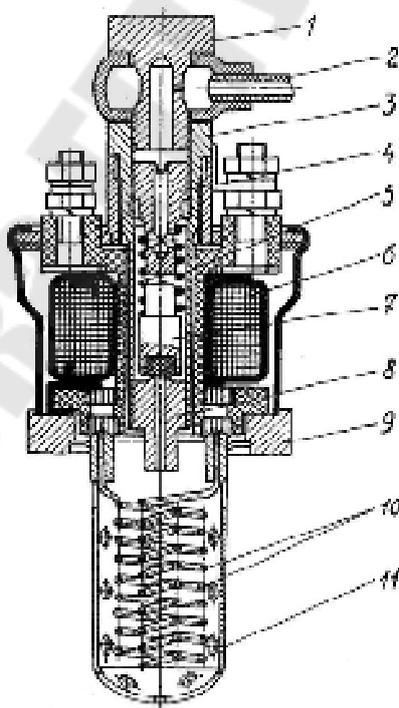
Подогреватель электрофакельный: 1 – болт; 2 – трубка топливная; 3 – корпус клапана; 4 – штуцер; 5 – пружина клапана; 6 – катушка электромагнита; 7 – клапан; 8 – седло клапана; 9 – корпус; 10 – спираль накаливания; 11 – колпачок
